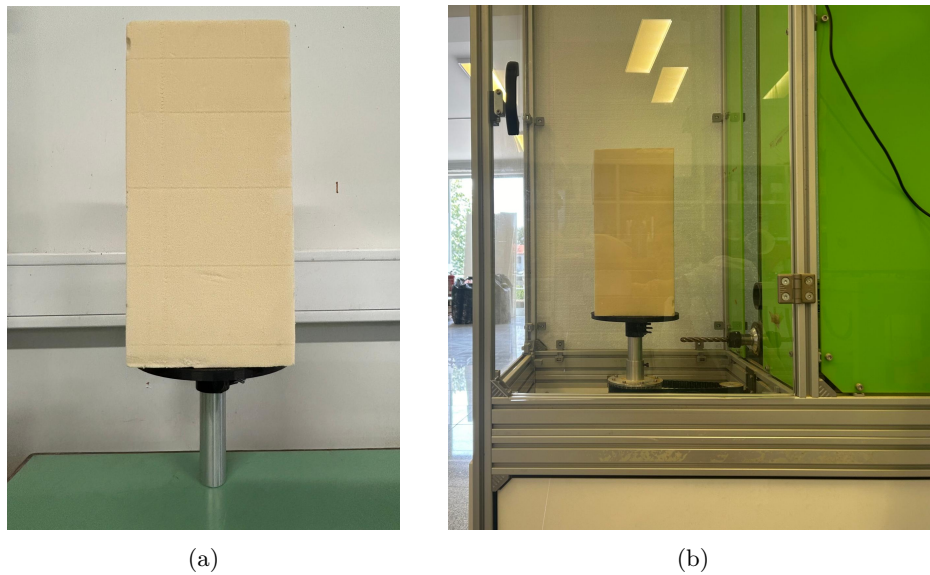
Bloco de PU fixado à peça de fixação (a) e colocado na máquina CNC no eixo A (b)
